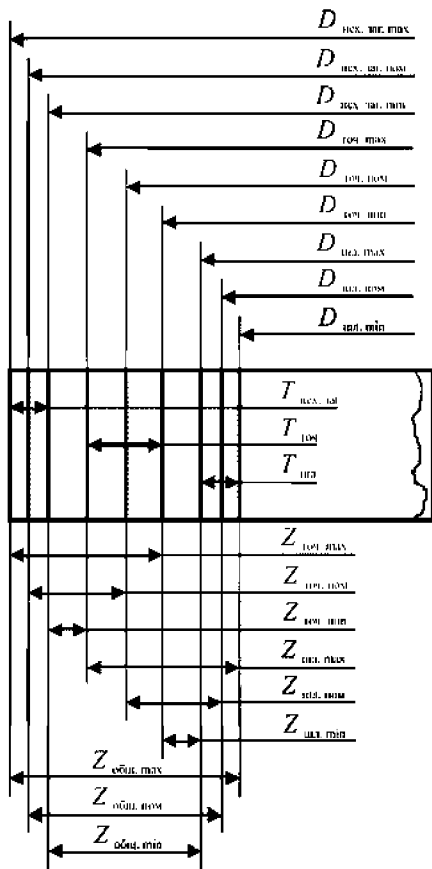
Схема расположения припусков и допусков на обработку заготовки вала точением и шлифованием:
